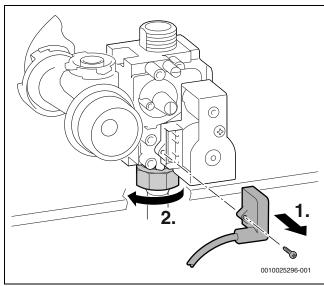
Retirer le connecteur et desserrer l'écrou-raccord
